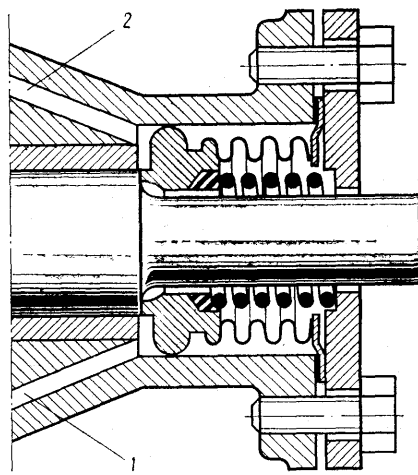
Сильфонный сальник, смонтированный в компрессоре:
